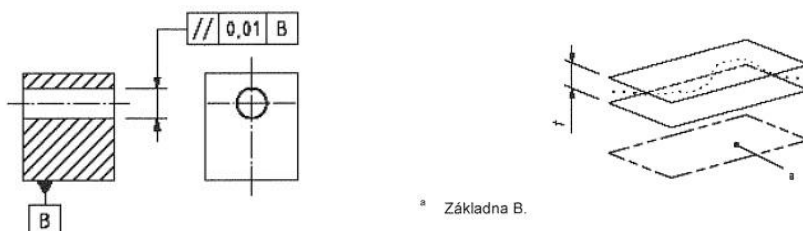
Označení a vysvětlení geometrické tolerance rovnoběžnosti [4]
